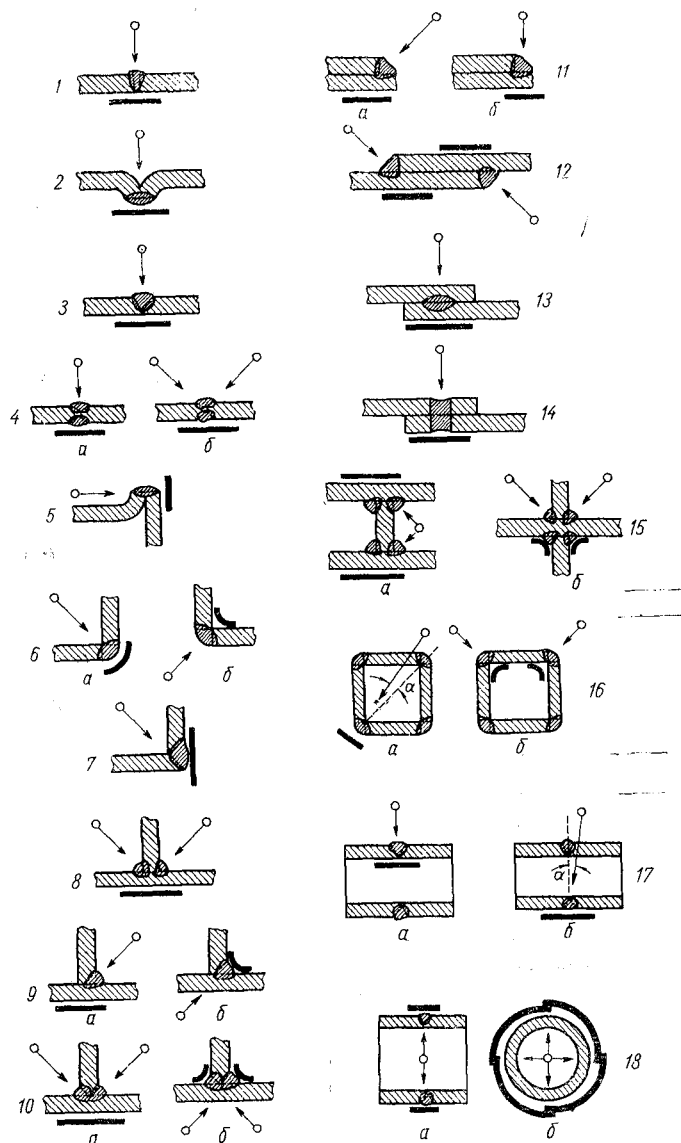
Типовые схемы просвечивания сварных изделий:
